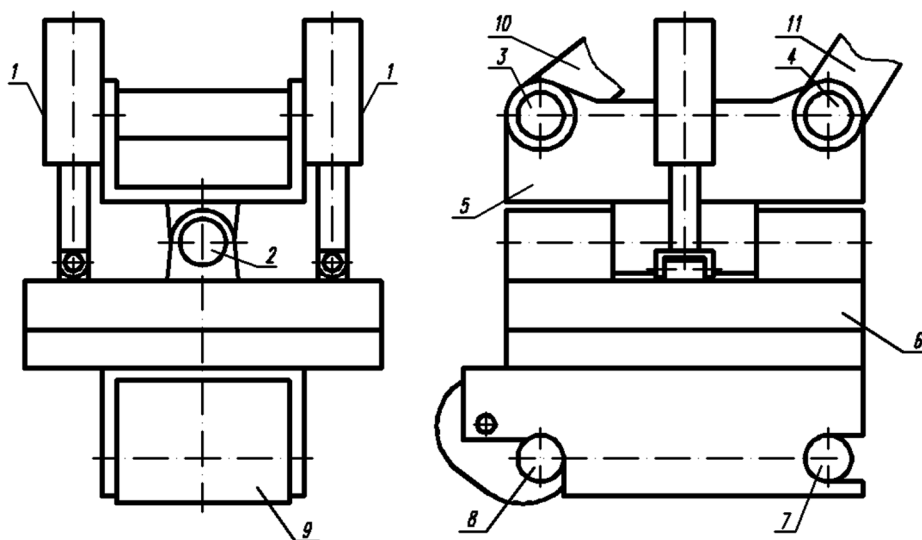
Схема захватного устройства: 1 – гидроцилиндры изменения угла ковша; 2 – ось; 3 и 4 – пальцы крепления захватного устройства на рабочем оборудовании экскаватора; 5 – корпус захватного устройства; 6 – поворотная платформа; 7 и 8 – пальцы крепления ковша к захватному устройству; 9 – крюк; 10 – тяга механизма поворота ковша; 11 – рукоять.
